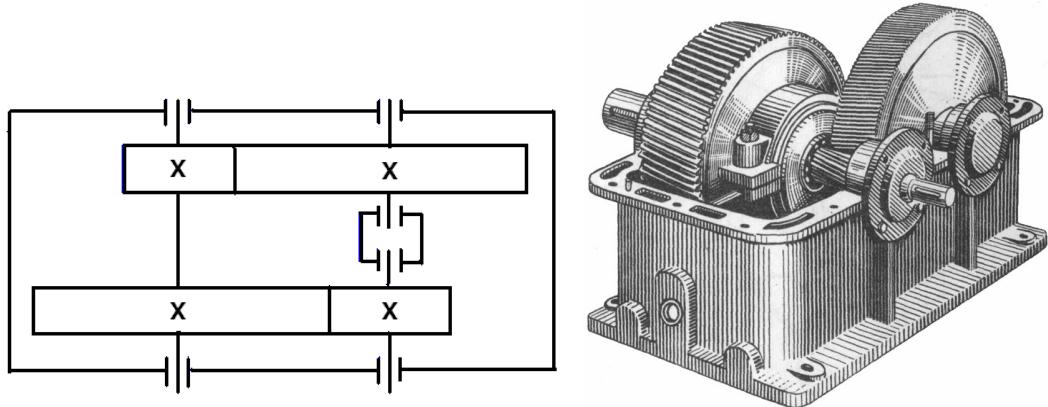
Цилиндрический соосный двухступенчатый редуктор
